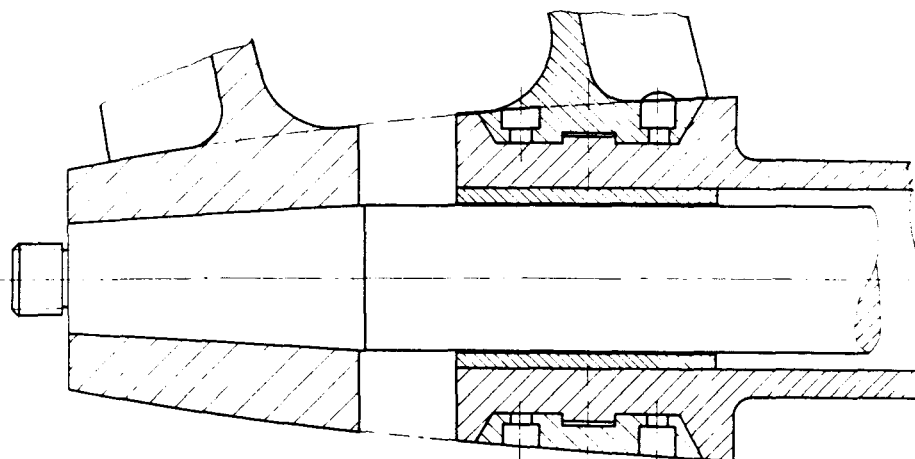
Befestigung von gegenläufigen Propellern; hinterer Propeller mittels paßfederlosem Öldruck-Schrumpfsitz befestigt, vorderer Propeller als gebauter Propeller mit einzeln an die Wellennabe geflanschten Flügeln ausgeführt.
